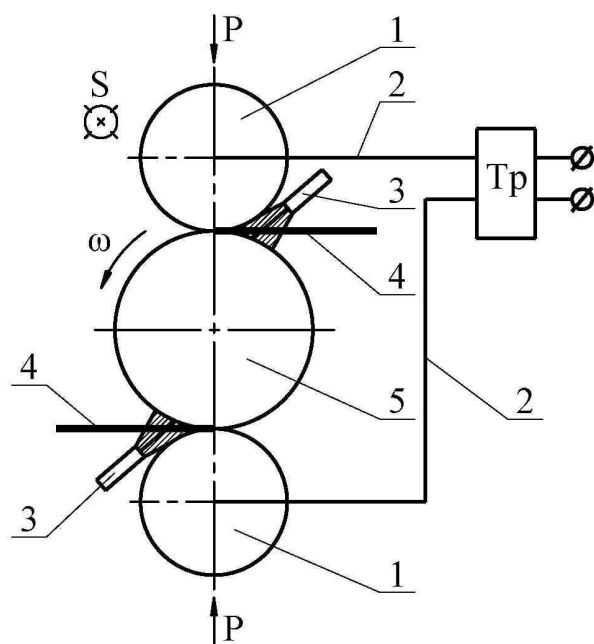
Схема установки УЭН-01: 1 – роликовый электрод; 2 – кабель от сварочного трансформатора; 3 – подача охлаждающей воды в зону приварки; 4 – присадочная проволока; 5 – заготовка; Tr – трансформатор; S – продольная подача роликовых электродов; P – сила прижима роликовых электродов
